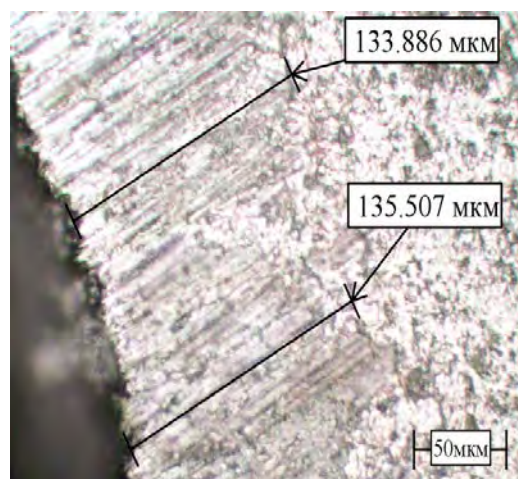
Изображение режущей кромки образца AZT-3 с нанесением размеров
